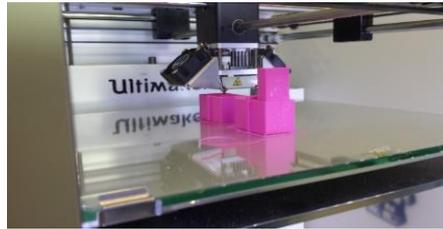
Technique d'impression par dépôt de matière. Crédit photo K.Ravari
